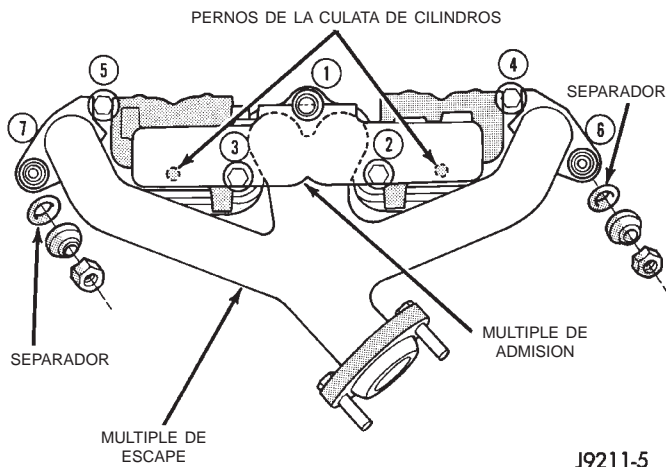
Desmontaje e instalación de los múltiples de admisión y escape—motor 2.5L
